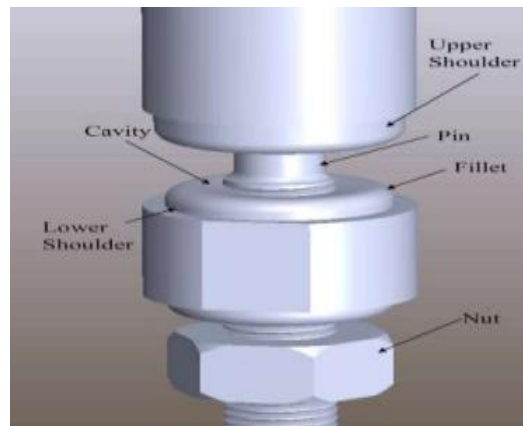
Détails concernant l'outil de soudage par friction Malaxage auto-réactif
